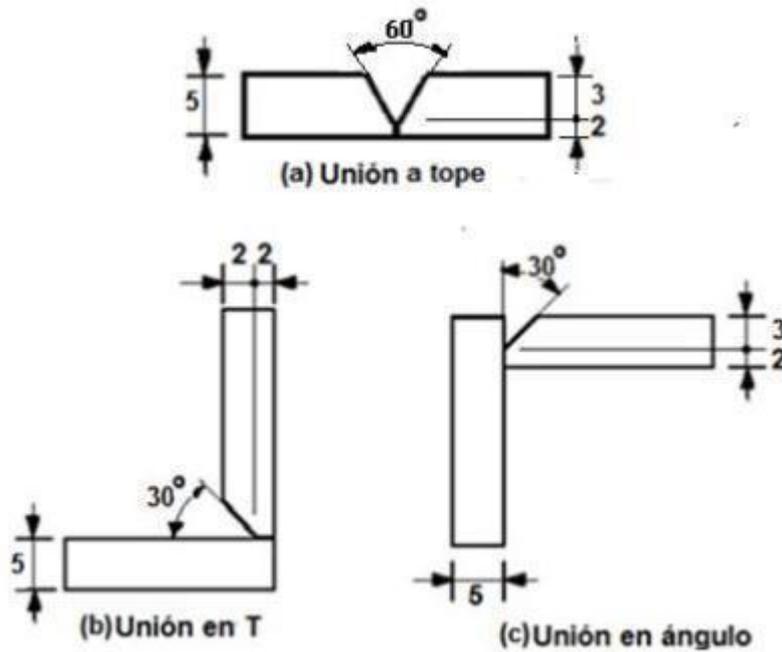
Tipos de juntas de soldadura.
